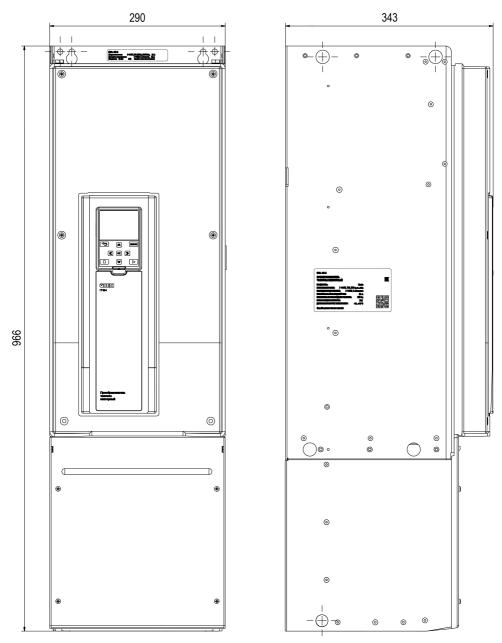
Габаритные размеры прибора в корпусе 5
